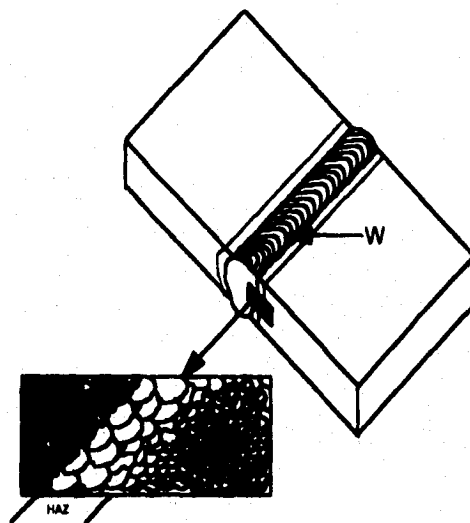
, soldadura realizada en una placa de acero, mostrando el metal de soldadura (W) y el calentamiento en la zona afectada (Haz)
